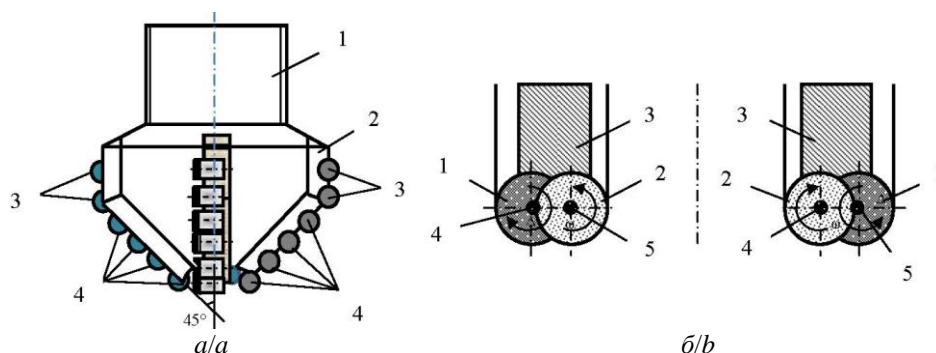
Породоразрушающий инструмент с вращающимися при бурении резцами типа PDC: а) буровое долото: 1 – корпус с резьбой; 2 – матрица; 3 и 4 – вращающиеся резцы; б) буровая коронка: 1 – наружный скважинообразующий резец; 2 – внутренний кernoобразующий резец; 3 – матрица коронки; 4 – ось вращения внешних скважинообразующих резцов; 5 – ось вращения внутренних кernoобразующих резцов; 6 – элементы каркаса осей вращения резцов
